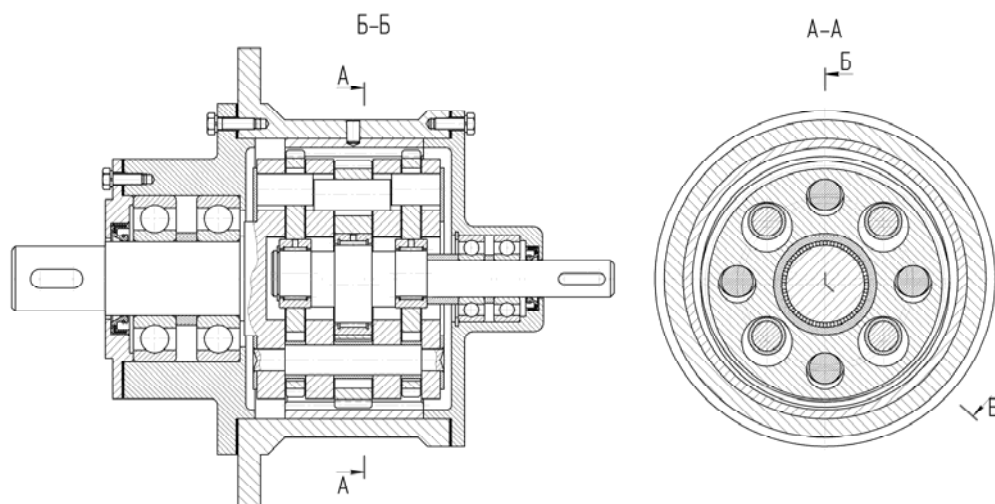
Конструкция планетарной передачи с роликовым механизмом снятия движения с сателлитов
